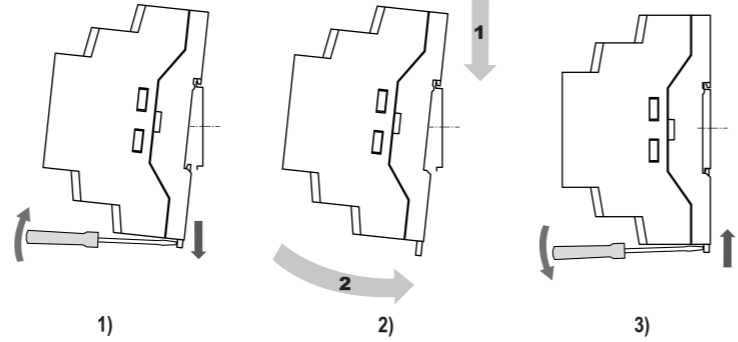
Монтаж прибора с креплением на DIN-рейку
